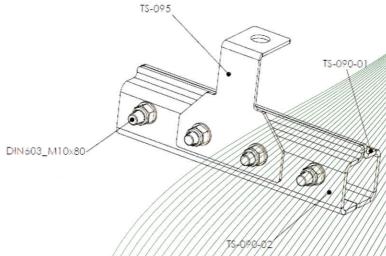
Anschlageinrichtung, Typ; TS STFA ZS
